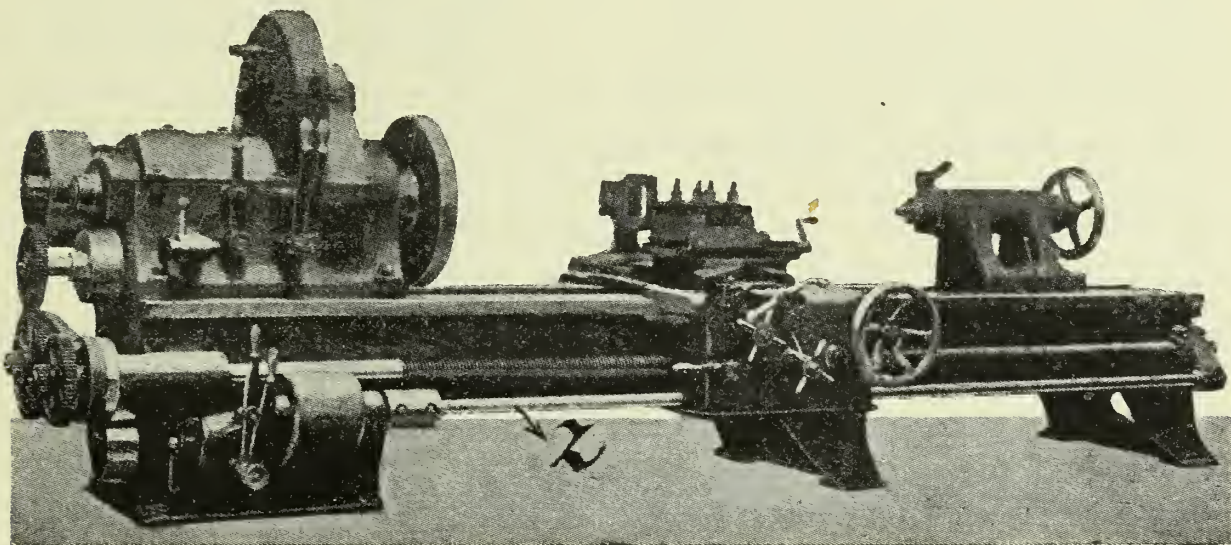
12" Schnelldrehbank der Tangye tool Co.
